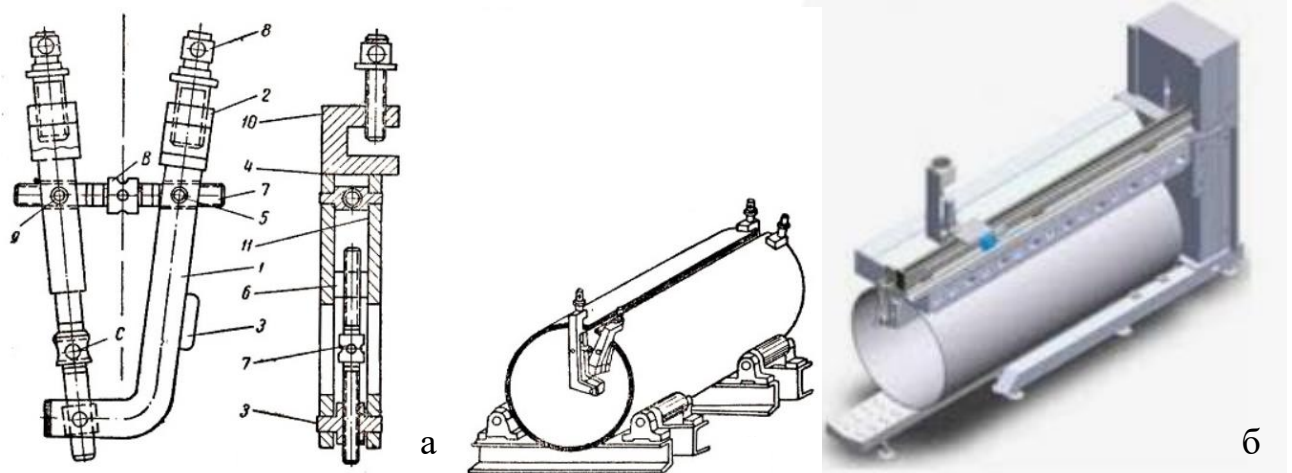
Струбцина для збирання обичайки: а – схема складання обичайки: 1 – колінчаста планка; 2 – скоба; 3 – накладка; 4 – планка; 5 – шарнірна гайка; 7 – стяжний гвинт; 8 – натискний гвинт; 9 – шарнірна гайка; 10 – скоба; 11 – планка; б – загальний вигляд струбцини
